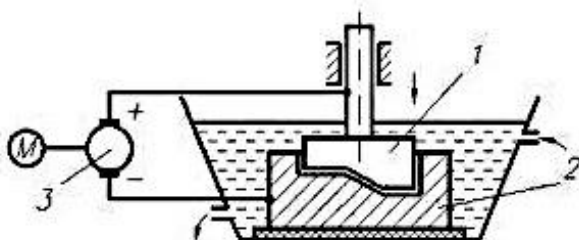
Принципиальная схема реализации электроимпульсных режимов обработки поверхностного слоя обрабатываемых деталей [235]
